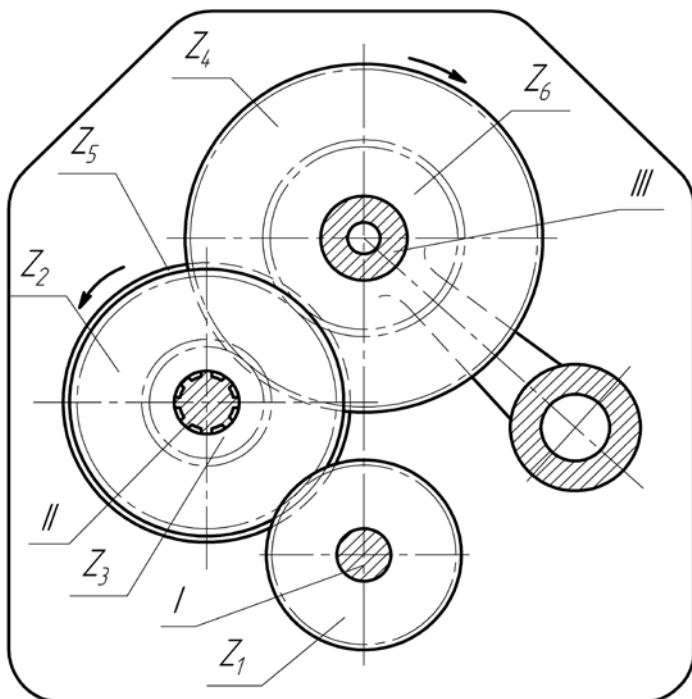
Свертка центральной шпиндельной бабки горизонтального многоцелевого сверлильно-фрезерно-расточного станка с ЧПУ
